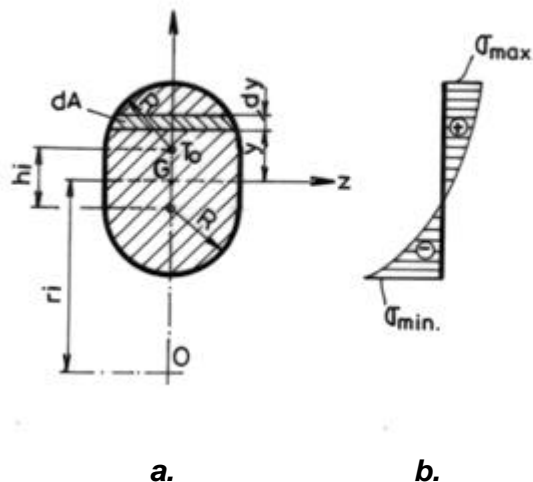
Secțiunea transversală a biglului în zona de bară curba.
